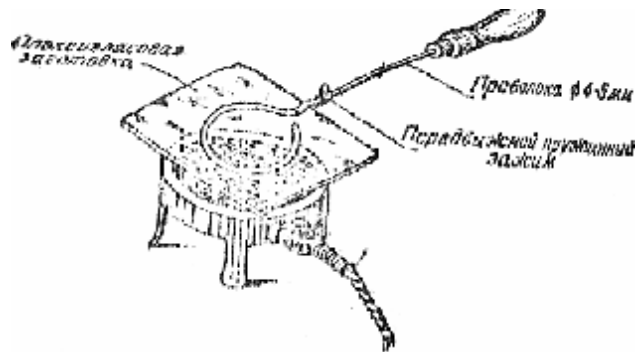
Приспособление для нагрева плексигласа на электроплитке
